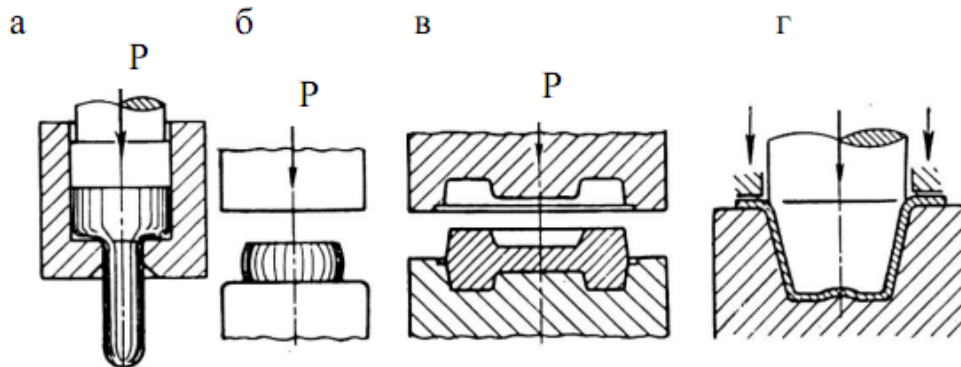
Способы получения заготовок обработкой давлением: а – прессование; б – свободная ковка; в – горячая объемная штамповка; г – холодная листовая штамповка
